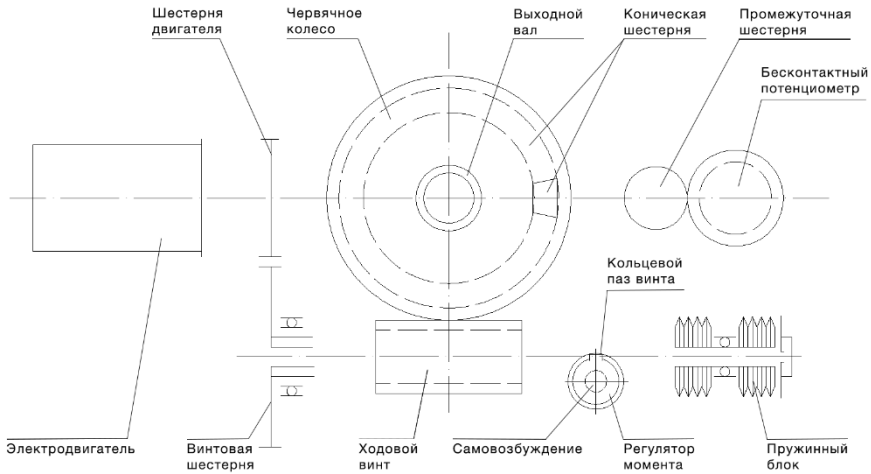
Кинематическая схема многооборотного привода (МТ)
